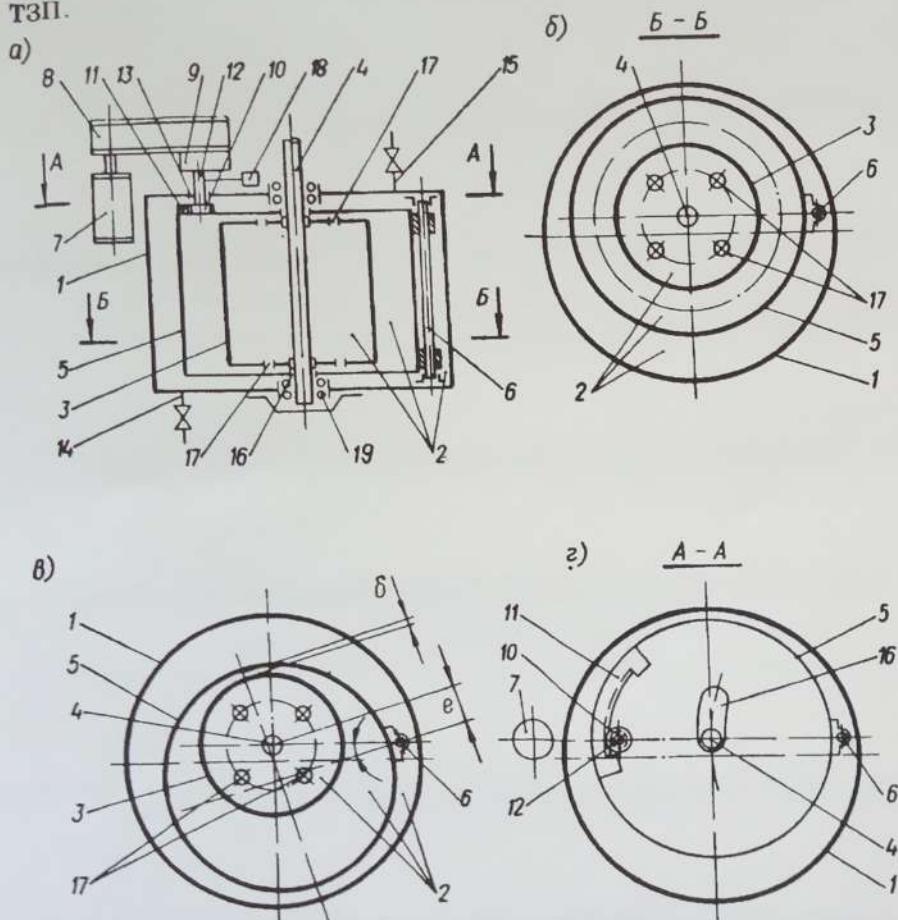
Схема гідрогальма [10]: а - осьовий розріз; б - поперечний розріз при співвісному положенні ротора і статора; в - те ж, при неспіввісному положенні; г - поперечний розріз з елементами механізму для переміщення статора: 1 - корпус; 2 - робоча рідина; 3 - ротор; 4 - вал ротора; 5 - статор; 6 - вісь статора; 7 - привід статора; 8 - редуктор; 9 - реверс; 10 - шестерня; 11 - зубчастий сегмент; 12 - вал реверса; 13 - сальник; 14 і 15 - патрубки; 16 і 17 - отвори; 18 - лічильник числа обертів вала 12; 19 - підшипник.
